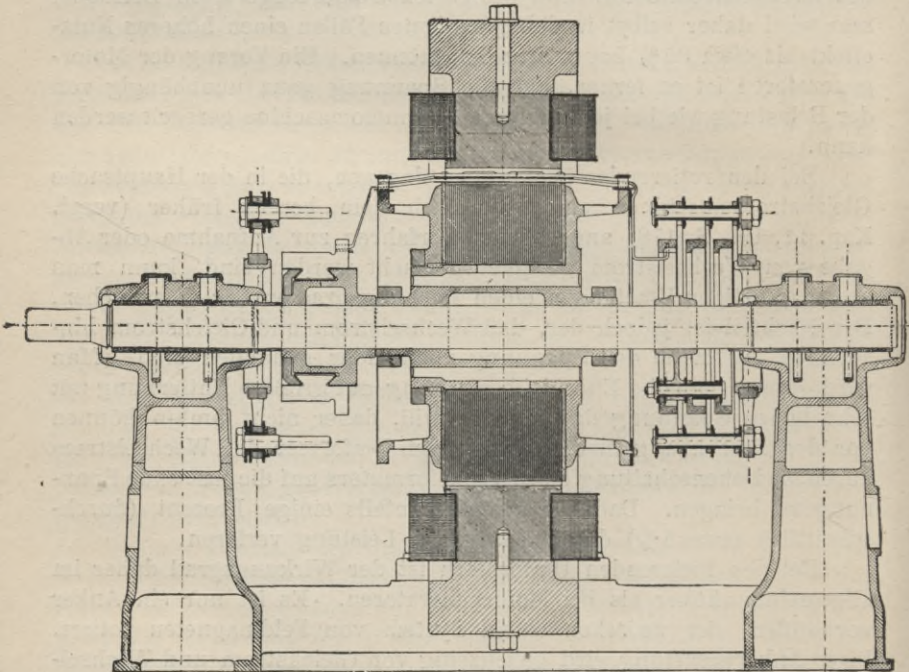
Rotierender Umformer von W. Lahmeyer & Co., A.-G., Frankfurt a. M.
